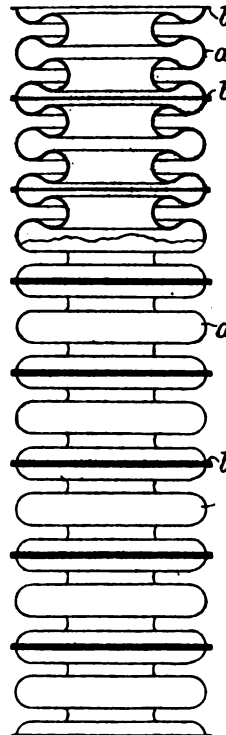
bis 32. Geschweißter Schlauch, schraubenförmig gewickelt.
